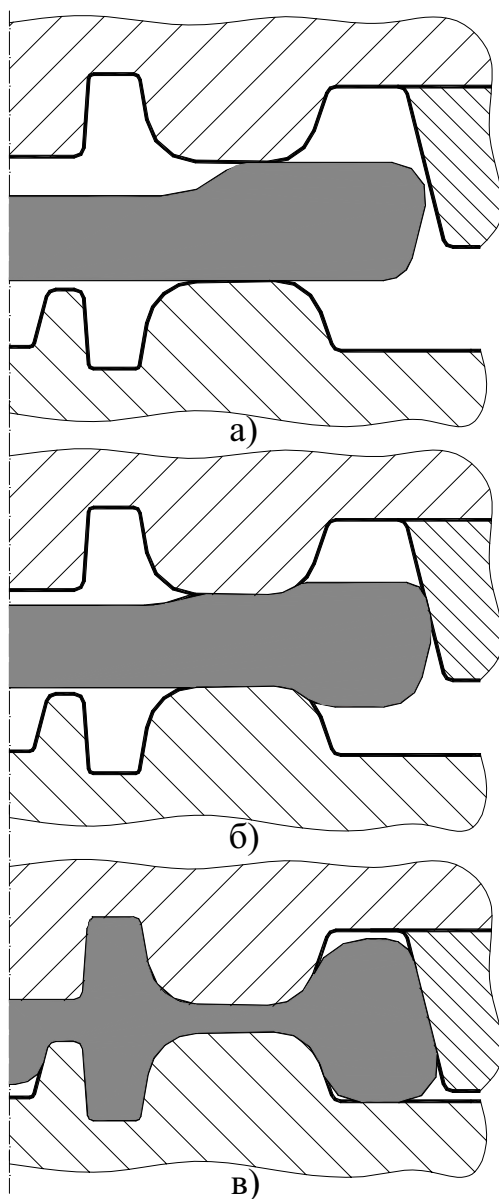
Существующая технология штамповки колесных заготовок.
